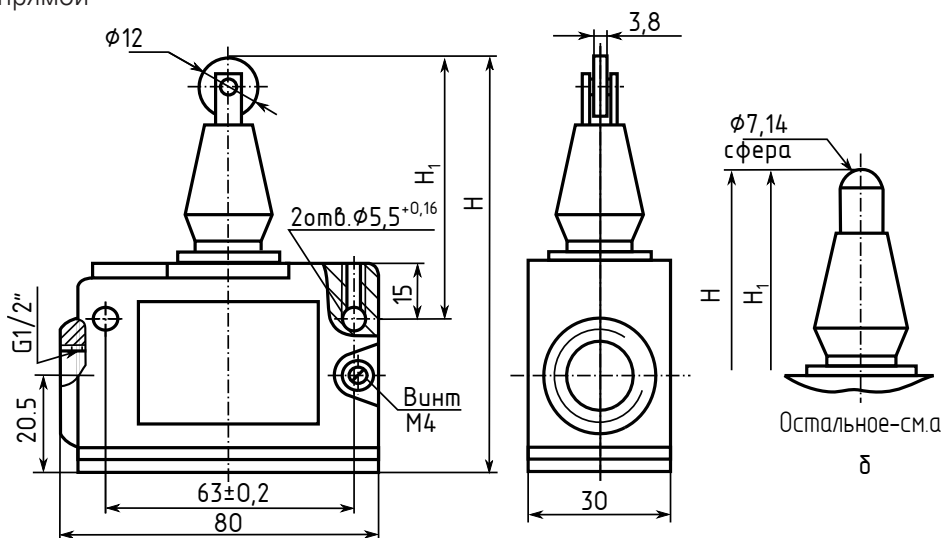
Габаритные, установочные и присоединительные размеры микровыключателей со степенью защиты IP54 с комбинированным креплением на поверхности, с монтажом проводов винтами или пайкой с приводом:
